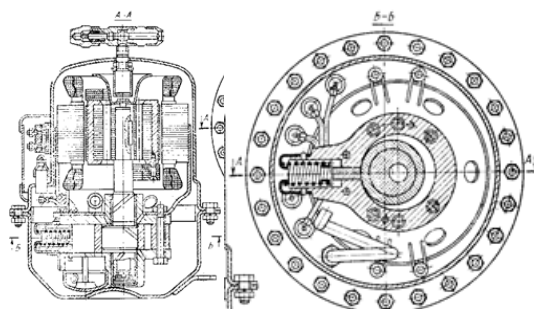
Полугерметичный холодильный компрессор с катящимся ротором
